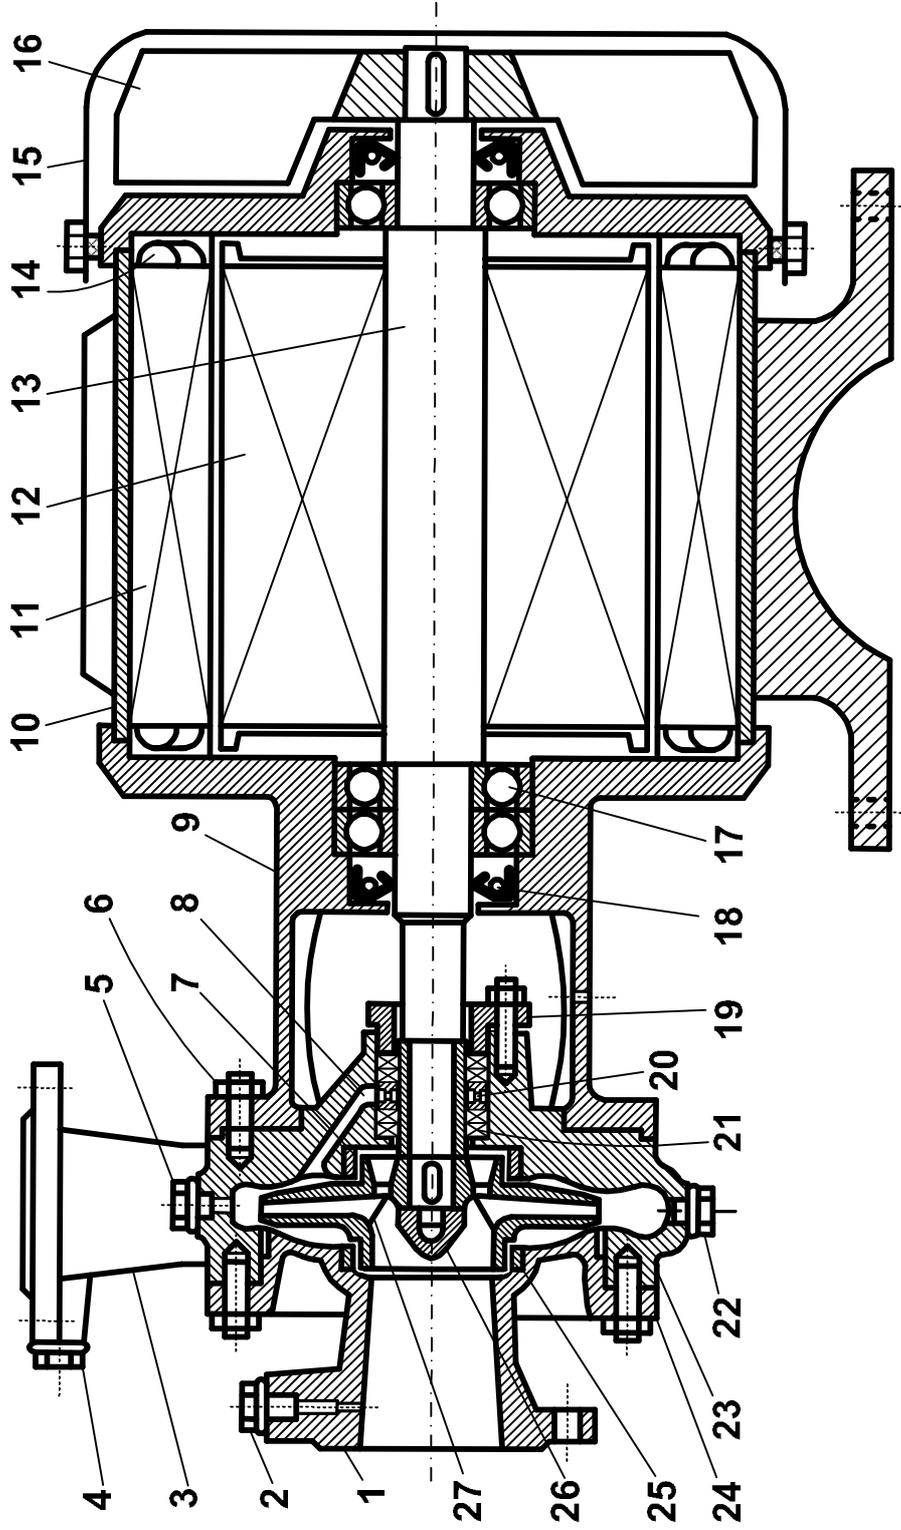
Моноблочный консольный насос с опорой на двигатель:
